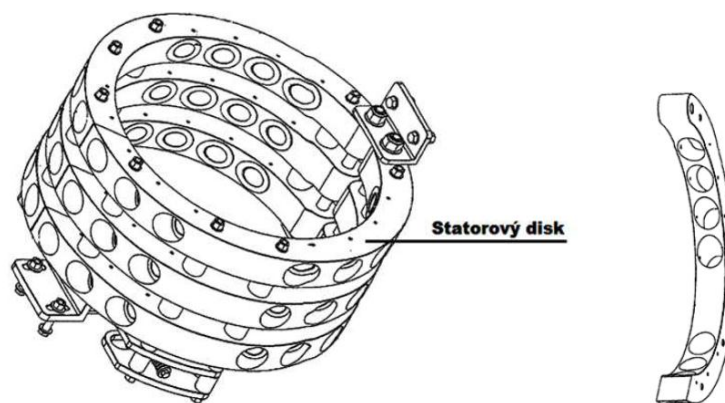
Posunutí magnetů u Perenděvova motoru [6]
